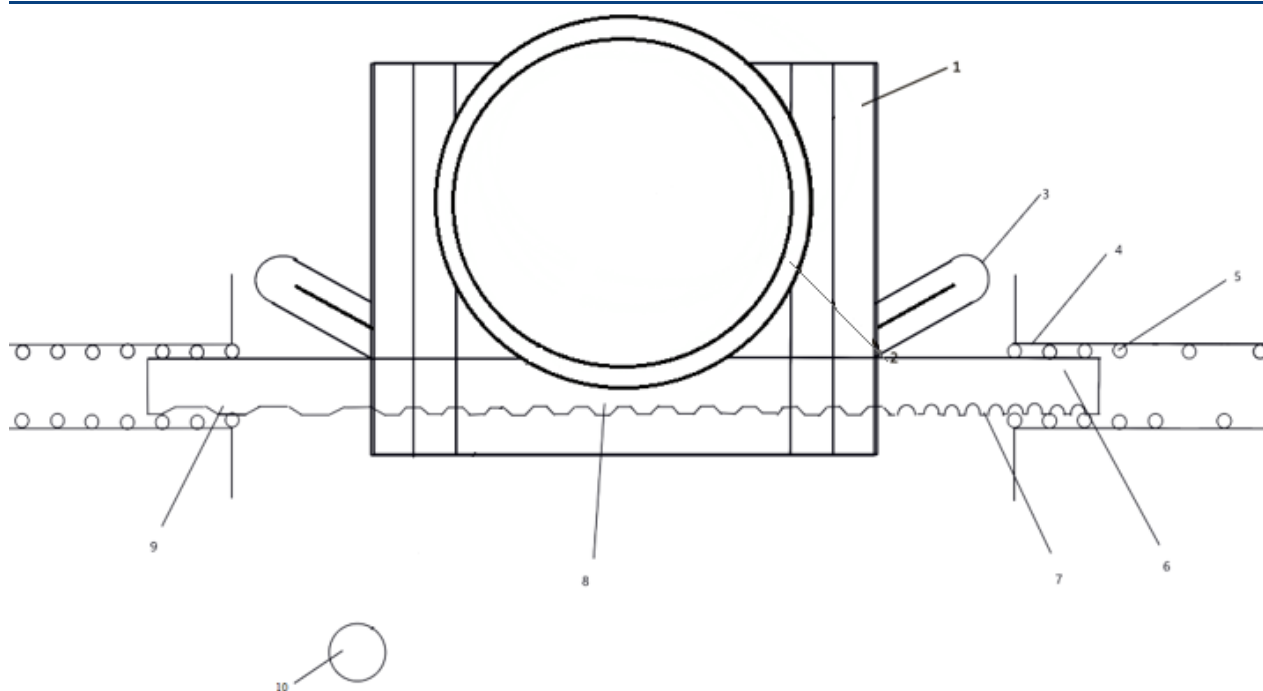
Общий вид индуктора линейного асинхронного двигателя. 1 – магнитопровод; 2 – зубчатое колесо; 3 – обмотка индуктора; 4 – направляющие; 5 – ролики; 6 – зубчатая рейка; 7, 8 и 9 – приставные гофрированные зоны; 10 – привод зубчатого колеса.
